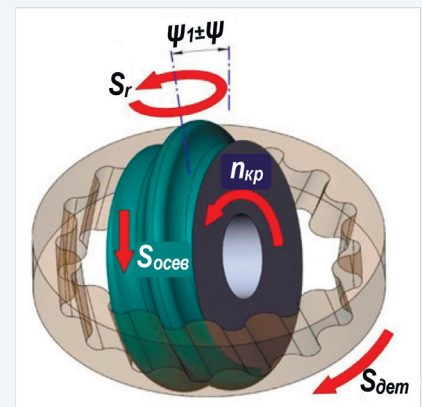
Схема изготовления внутреннего свободного профиля колеса с винтовыми зубьями глобидным червячным кругом
